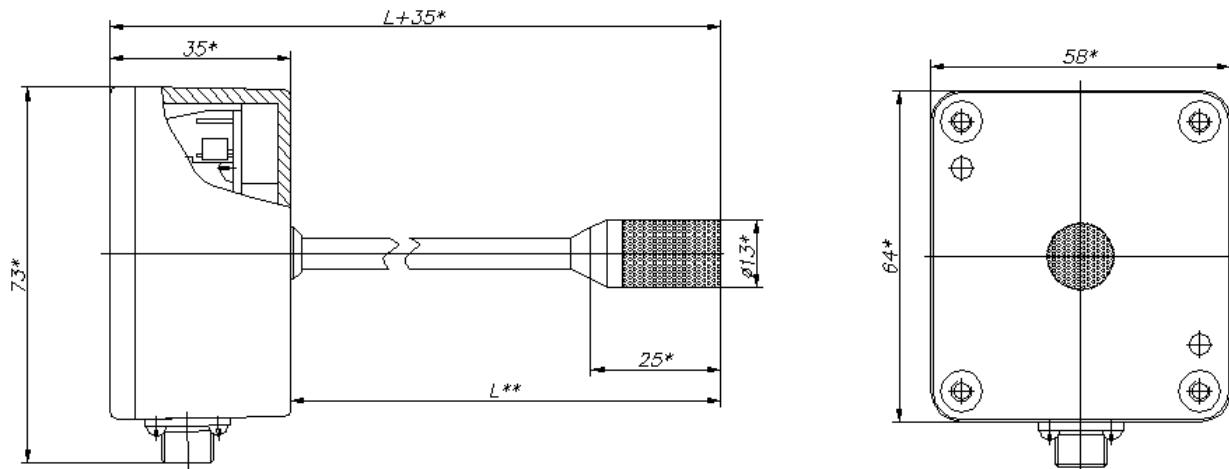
Измерительный преобразователь ИПВТ-03-14
